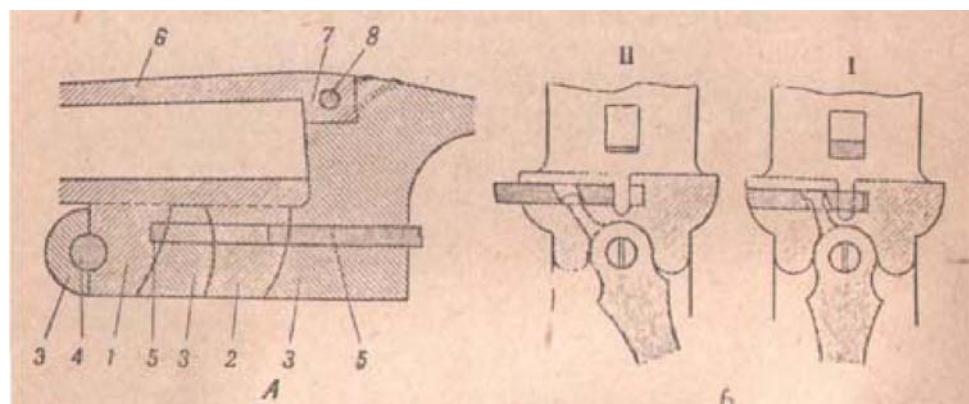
Тройной затвор (схема работы): А - схема точек крепления тройного затвора; 1, 2 - пол ствольные крюки; 3 - корпус колодки; 4 - осевой болт; 5 - рамка (засов); 6 - стволы; 7 - продолжение прицельной планки; 8 - поперечный болт (болт Гримера); Б - схема работы поперечного болта и рамки; I - стволы заперты; II - стволы освобождены
